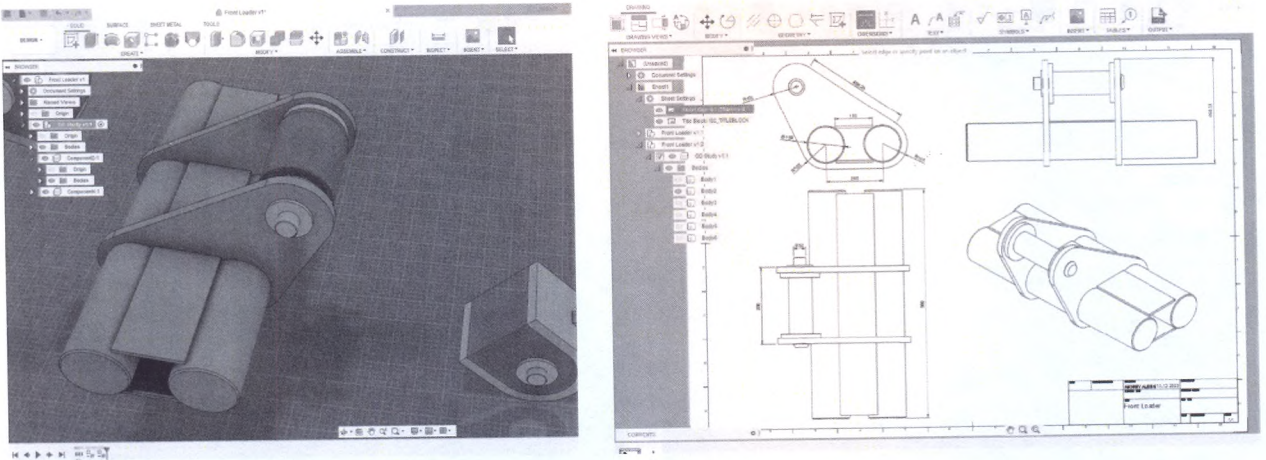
Изготовление чертежей по 3D-моделям в САМ
